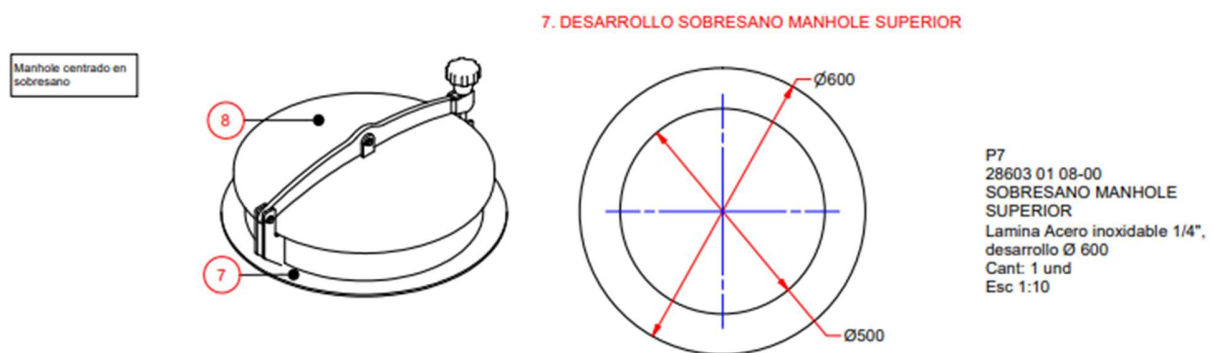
Desarrollo y corte de sobresano para *manhole* superior.
